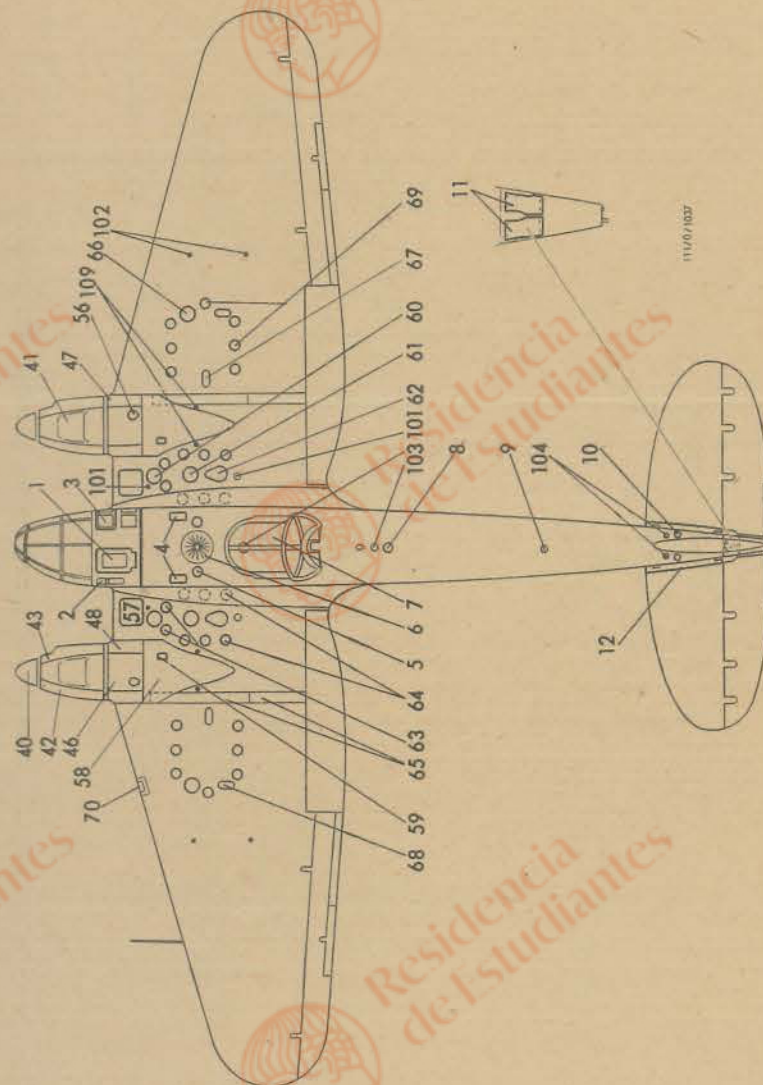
Deckel- und Klappenplan (Draufsicht)
